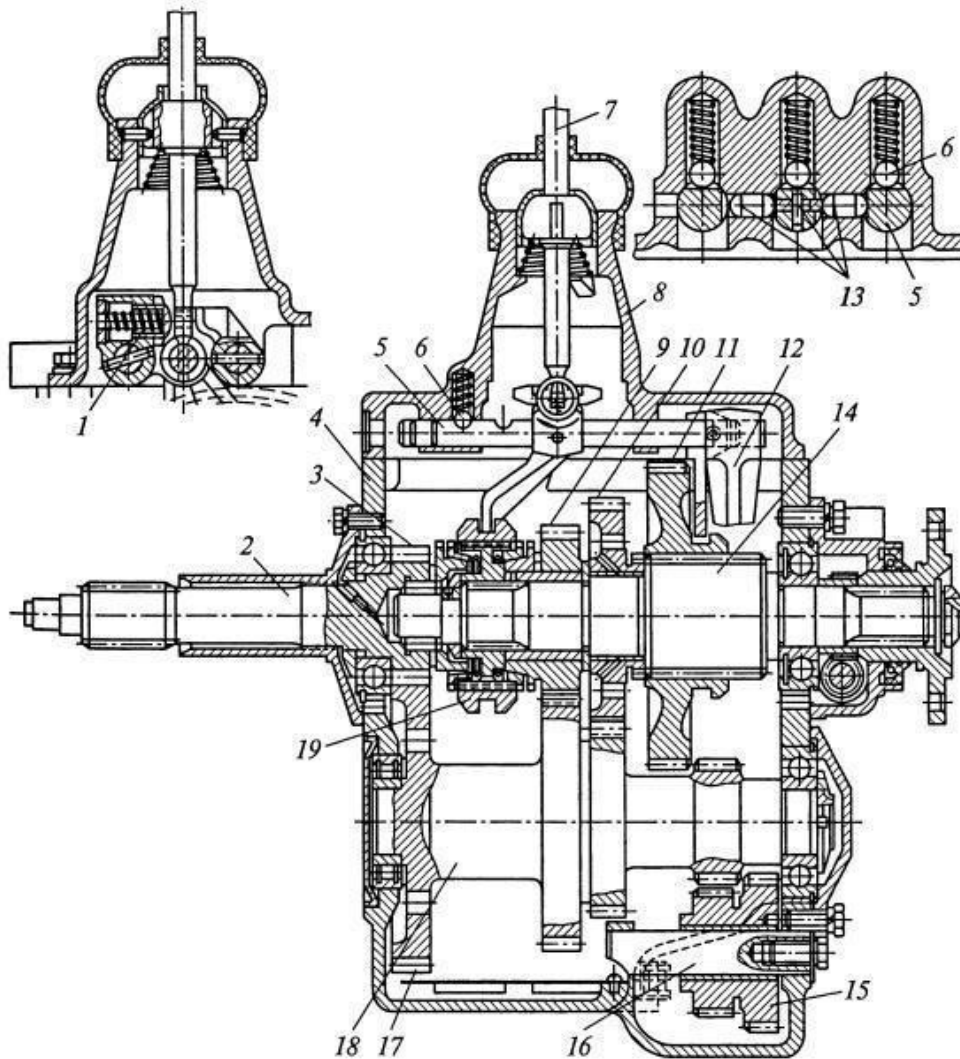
Коробка передач автомобиля ГАЗ-53А
